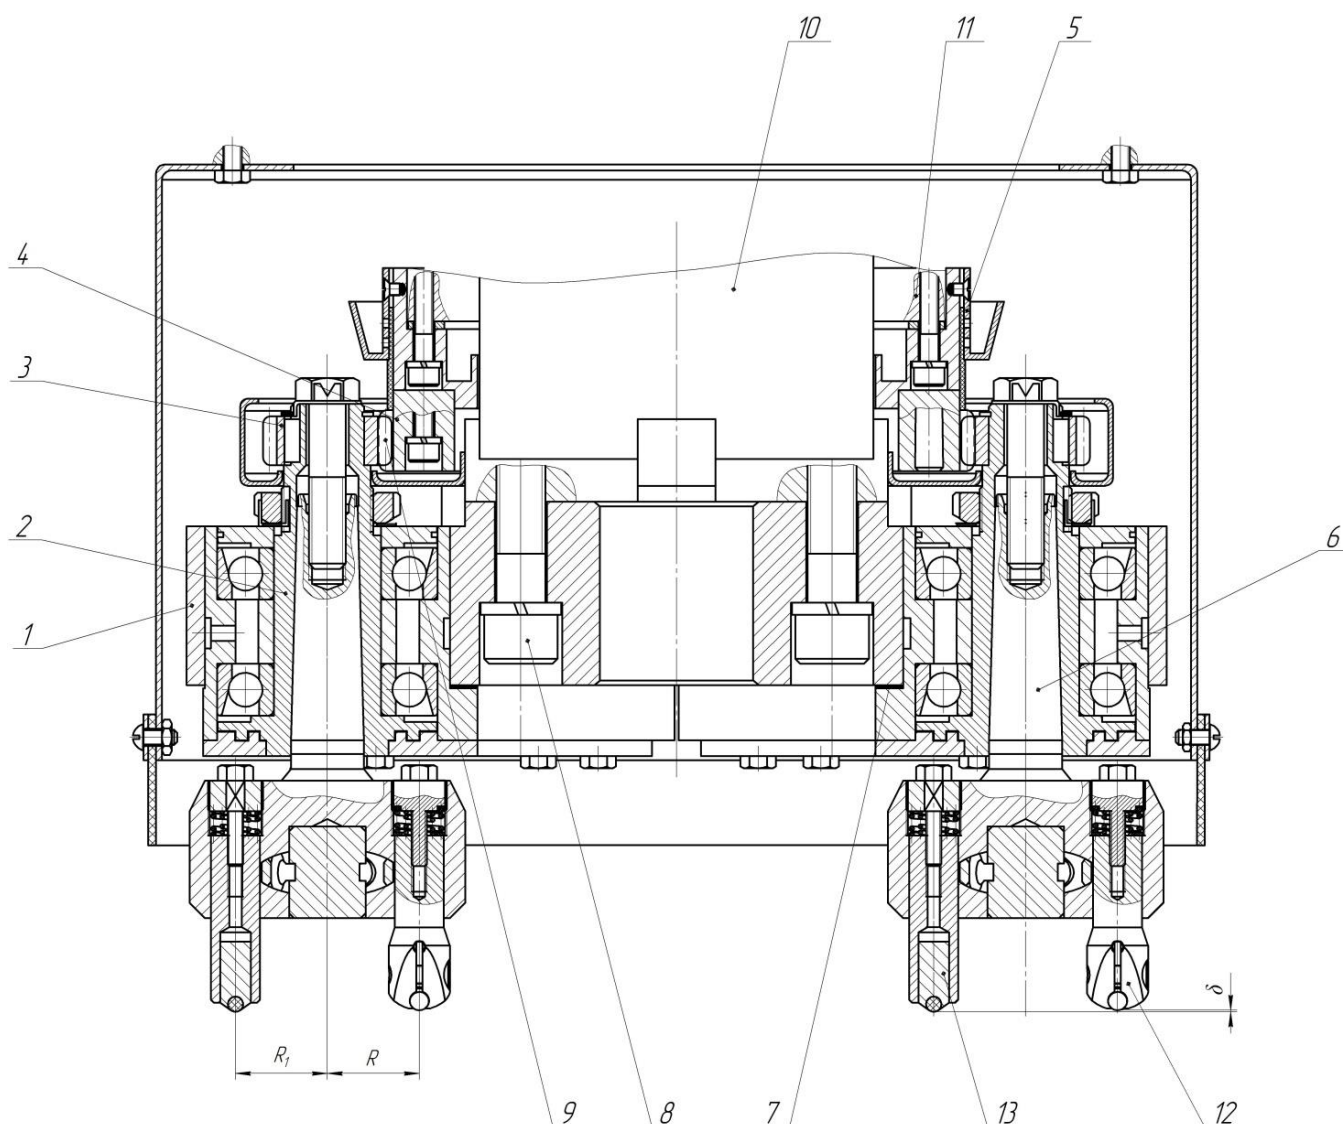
Інструмент для обробки плоских поверхонь, який може бути застосований для нестационарних умов обробки плоских поверхонь деталей
